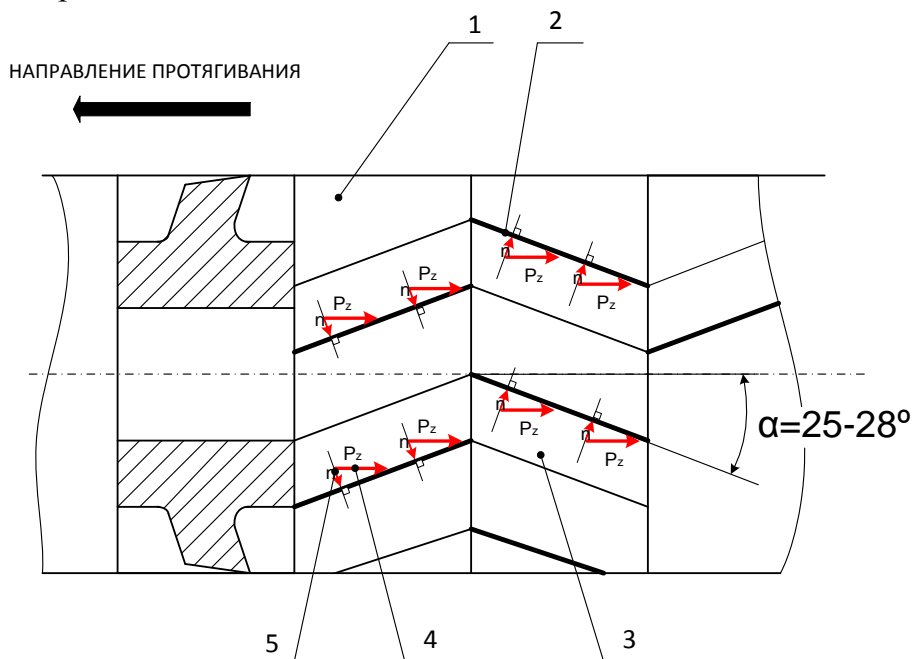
Протяжка для обработки глубоких отверстий со сменными режущими частями
